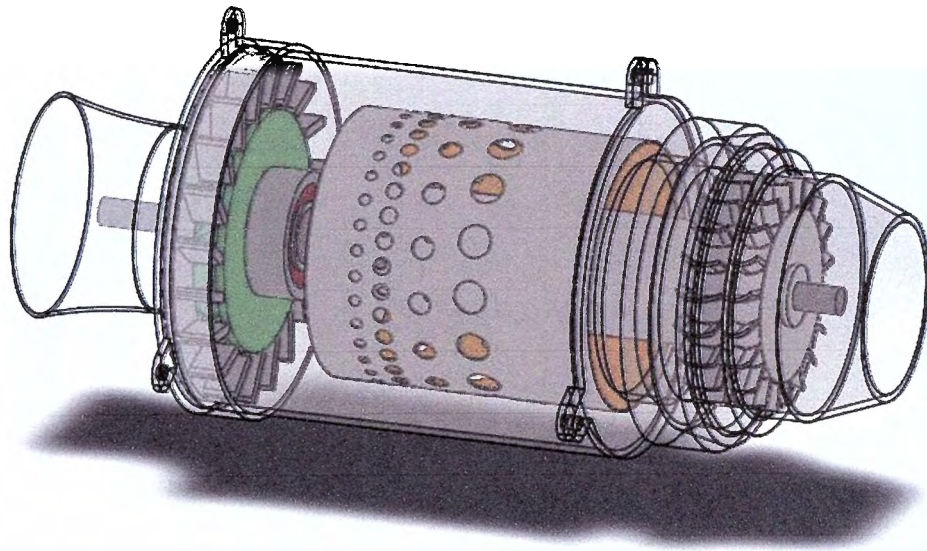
Ensemble de mini turbina MOBOR 81.
